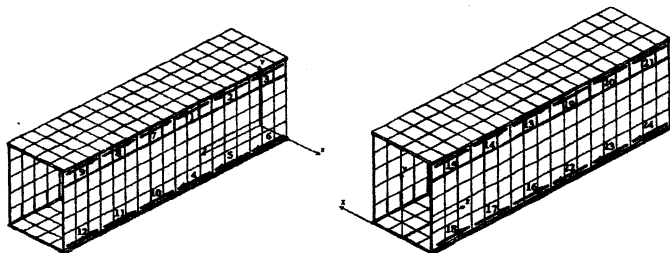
Обратноступенчатый порядок наложения сварных швов
